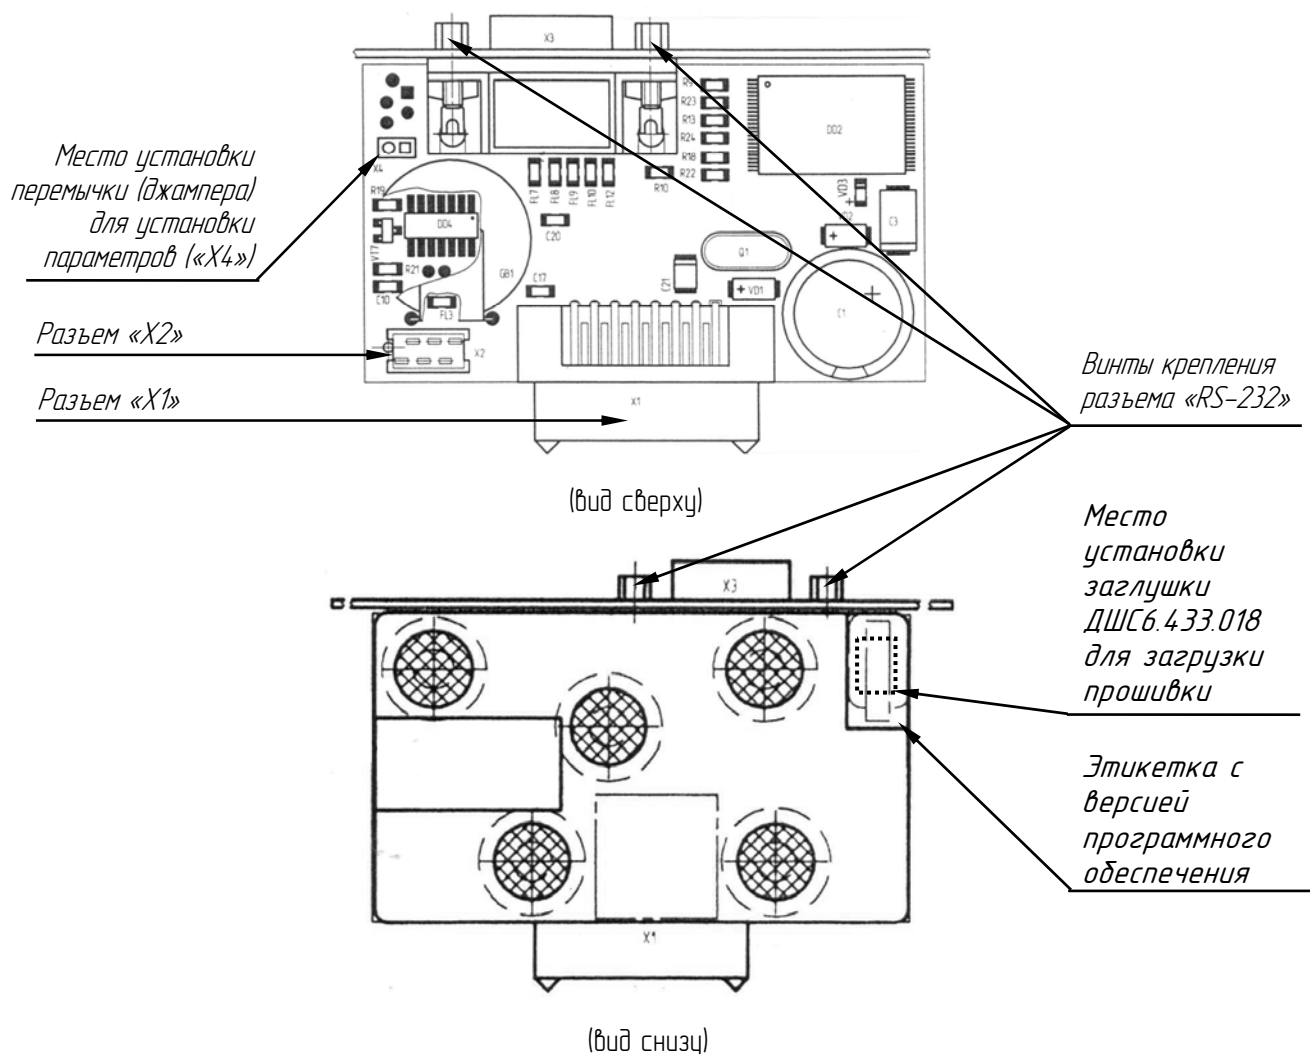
Виды контроллера фискального ДШС3.093.269
